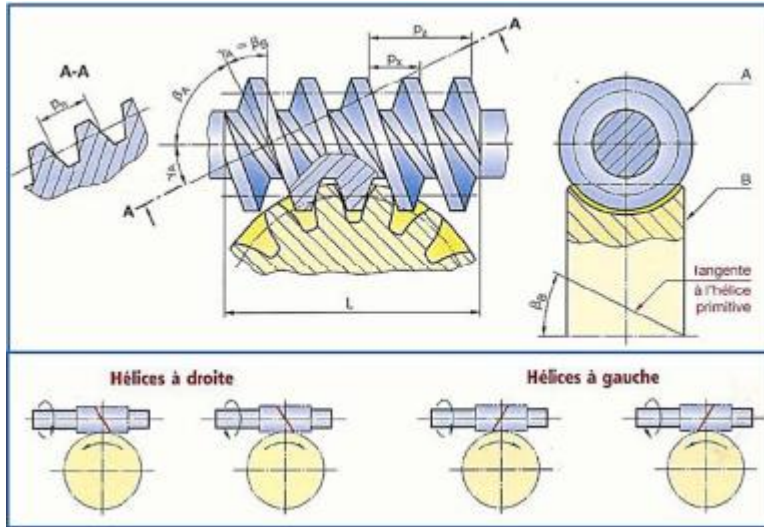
Engrenage gauche (roue et vis sans fin)
